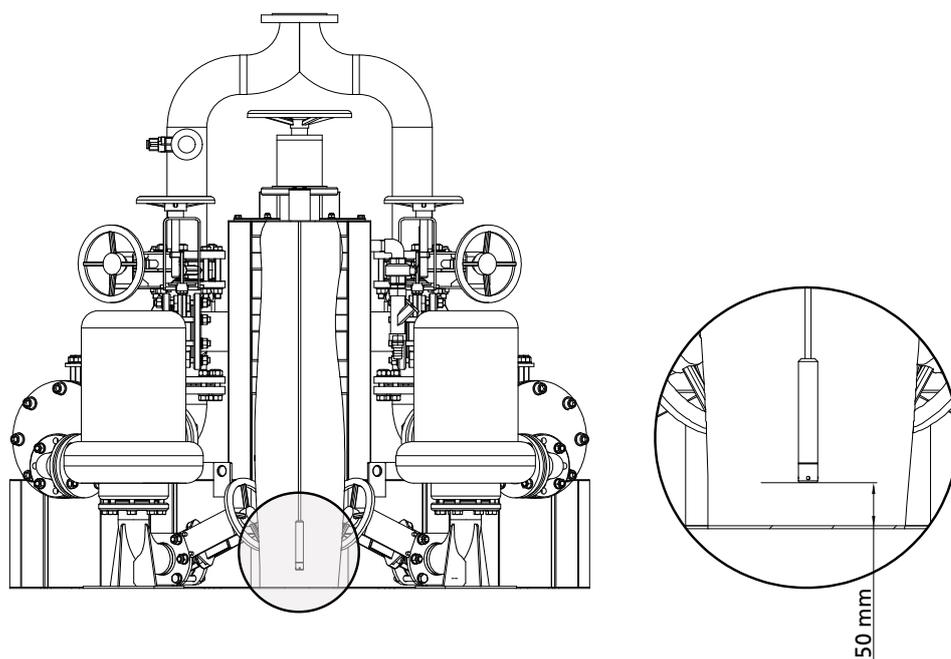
Montaje del sensor de nivel (ejemplo: AmaDS³ 02.10/2/01.11)
